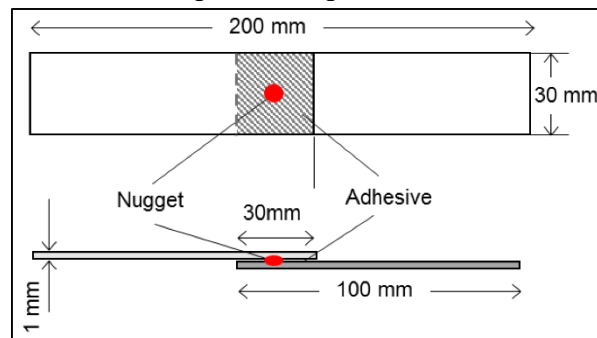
centrage de la pointe de soudage sur les pièces à souder
